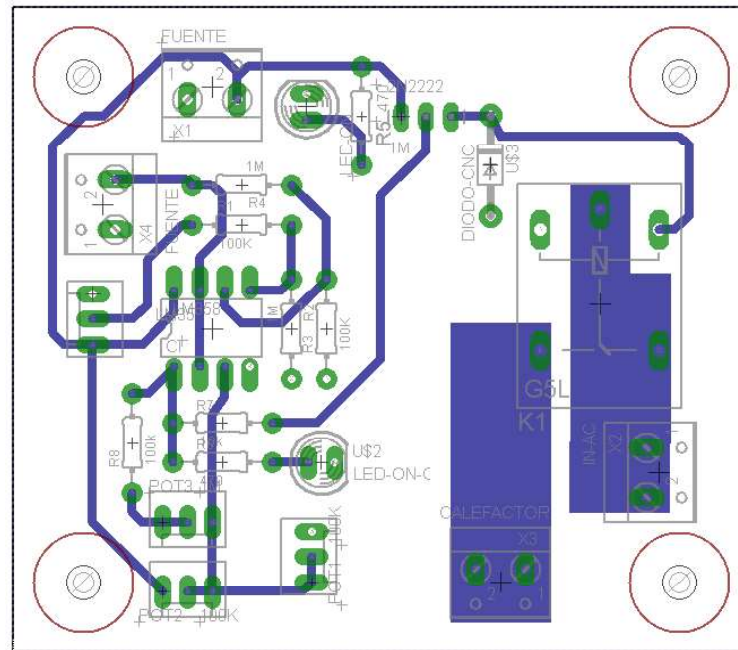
Diseño PCB de la tarjeta KIT INST-02.
